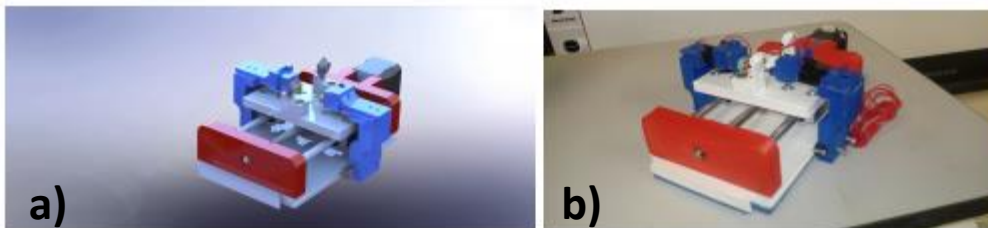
a) Diseño en SolidWorks, b) Diseño del prototipo real.
